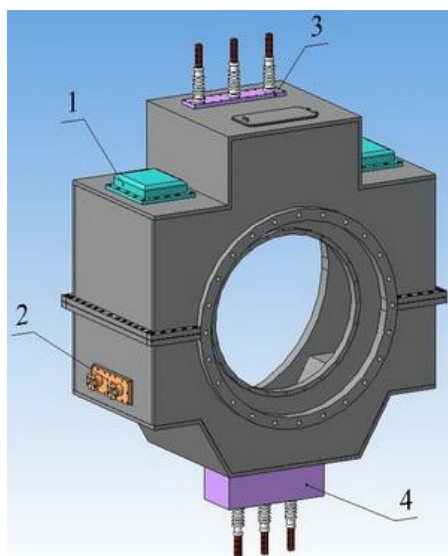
Эскиз конструкции приставного корпуса ТГ с замкнутой воздушной системой вентиляции: 1 – воздухоохладитель;
